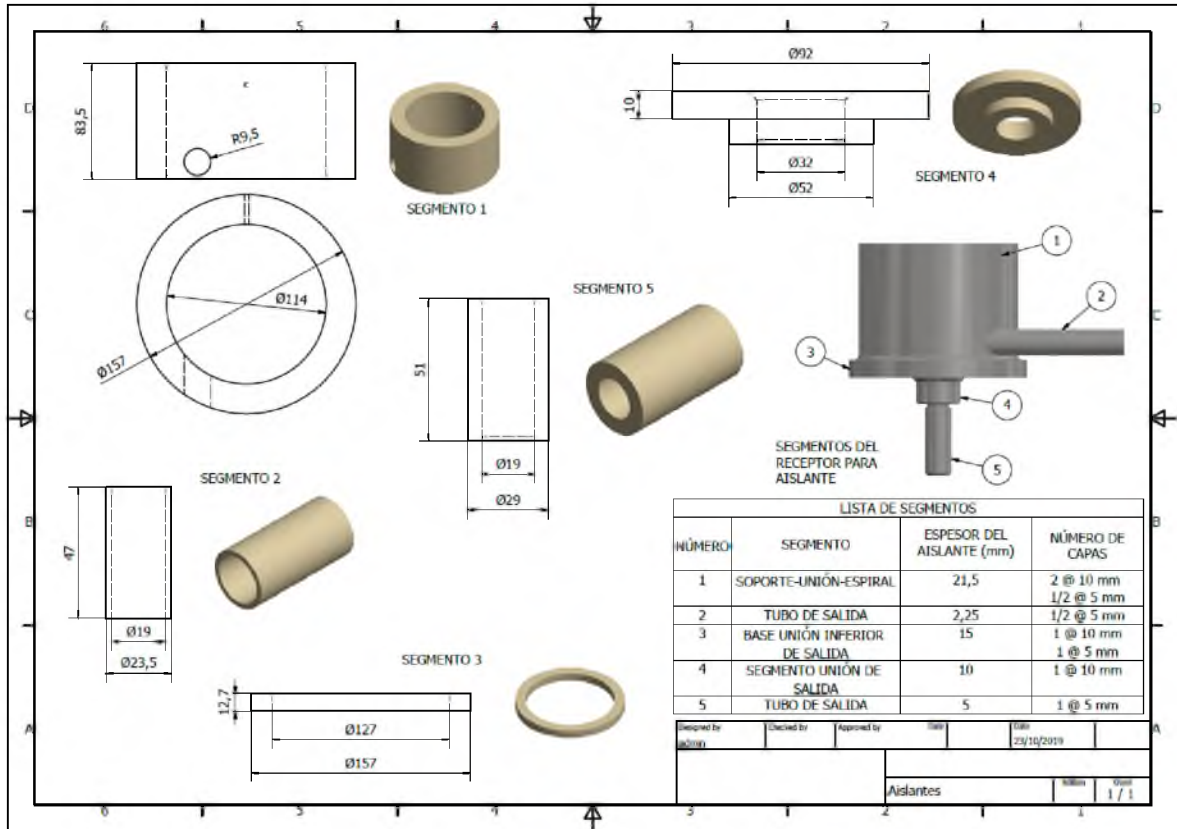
Segmentos y dimensiones (en mm) de aislante seleccionado para la protección del receptor solar.
